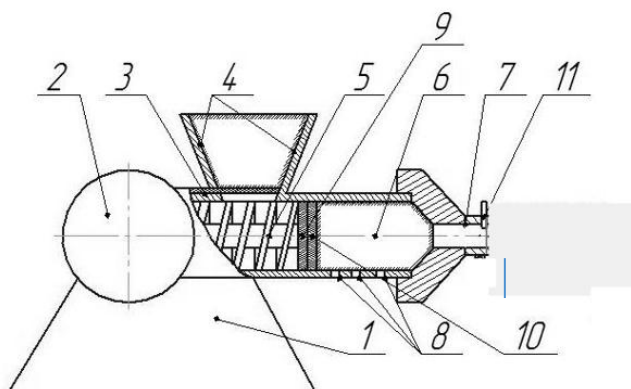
Пресс для изготовления брикетов из подстильного навоза: 1 – рама, 2 – электропривод, 3 – корпус пресса, 4 – загрузочный бункер, 5 – камера со шнеком, 6 – камера прессования, 7 – насадка, 8 – дренажные отверстия, 9 – противорежущая пластина, 10 – нож, 11 – шип
